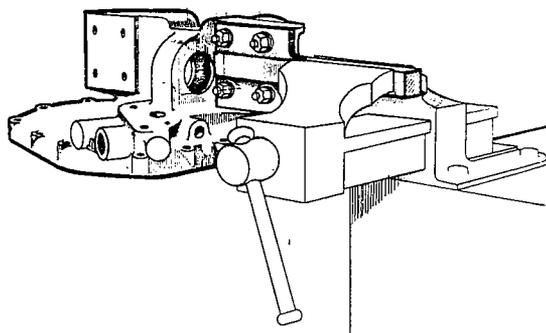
FIXATION DU CARTER ARRIÈRE DANS L'ÉTAU (9° VUE)
